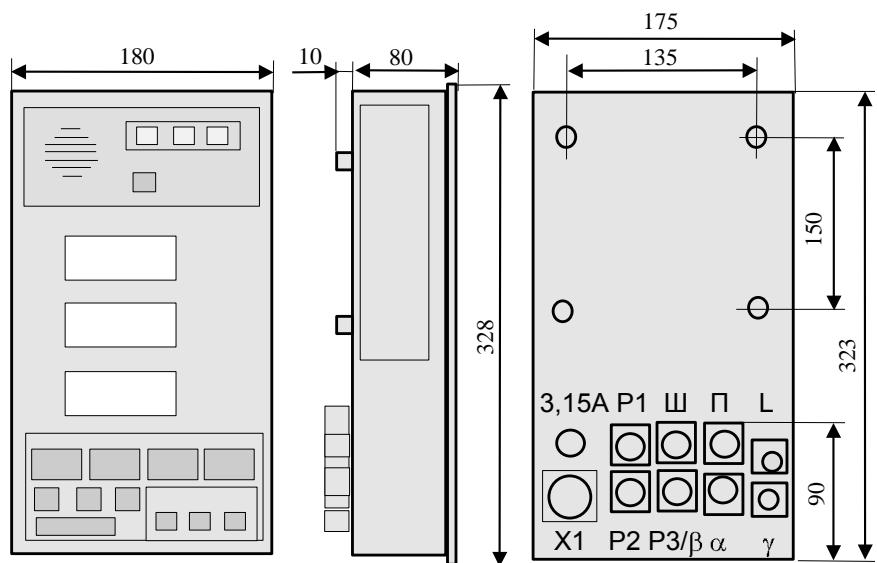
Габаритные и присоединительные размеры БОДа
